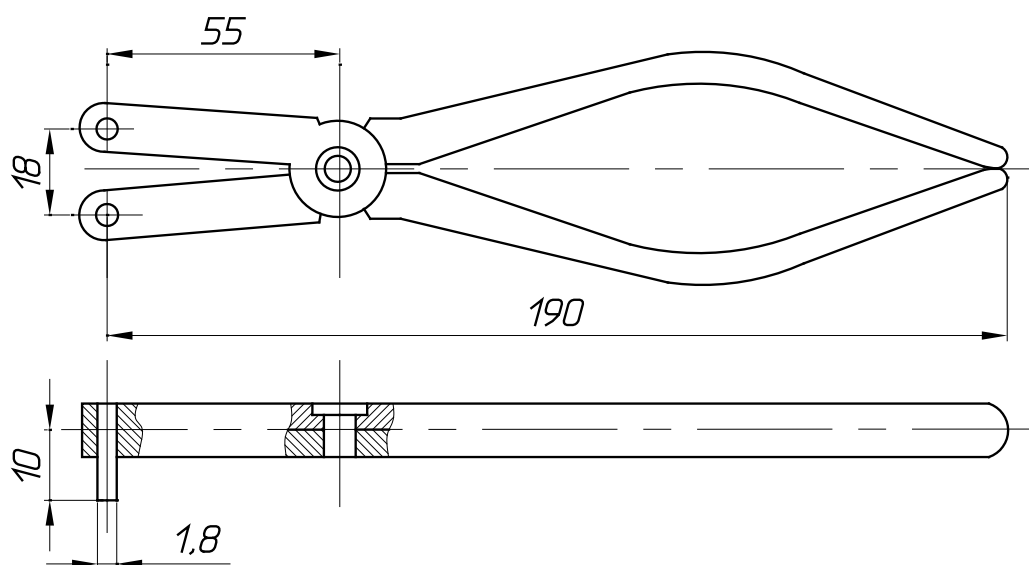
Щипцы для снятия и установки стопорных колец
